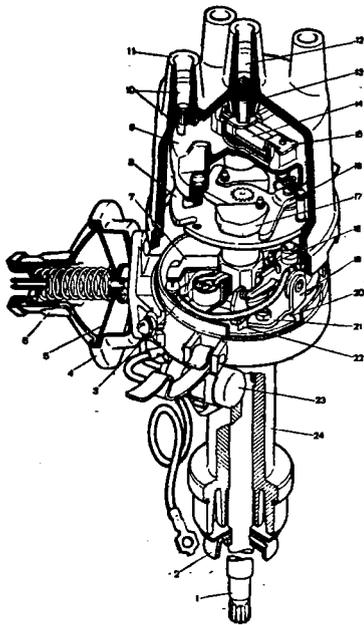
Распределитель зажигания 30.3706: 1 - валик; 2 - маслоотражательная муфта; 3 - фильц; 4 - корпус вакуумного регулятора; 5 - мембрана; 6 - крышка вакуумного регулятора; 7 - тяга вакуумного регулятора; 8 - опорная пластина центробежного регулятора; 9 - ротор распределителя зажигания; 10 - боковой электрод с клеммой; 11 - крышка; 12 - центральный электрод с клеммой; 13 - уголек центрального электрода; 14 - резистор; 15 - наружный контакт ротора; 16 - пластина центробежного регулятора; 17 - грузик; 18 - кулачок прерывателя; 19 - контактная группа; 20 - подвижная пластина прерывателя; 21 - винт крепления контактной группы; 22 - паз; 23 - конденсатор; 24 - корпус распределителя зажигания
